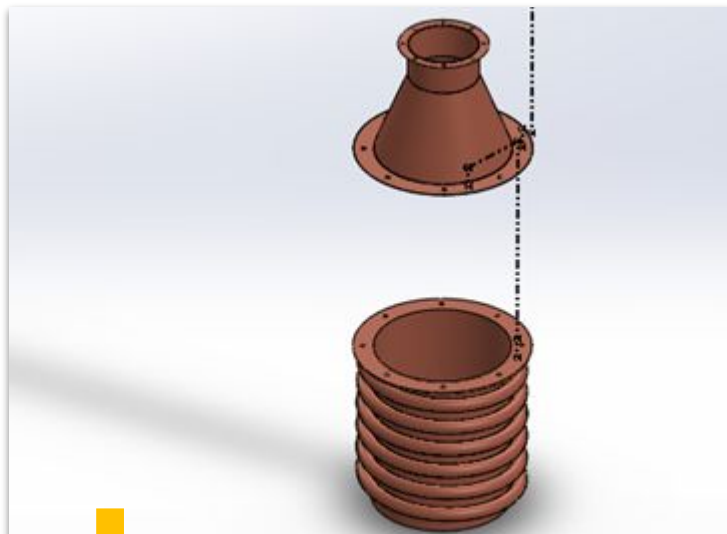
Vista explosionada del alambique con la espiral en el exterior y tapa.
